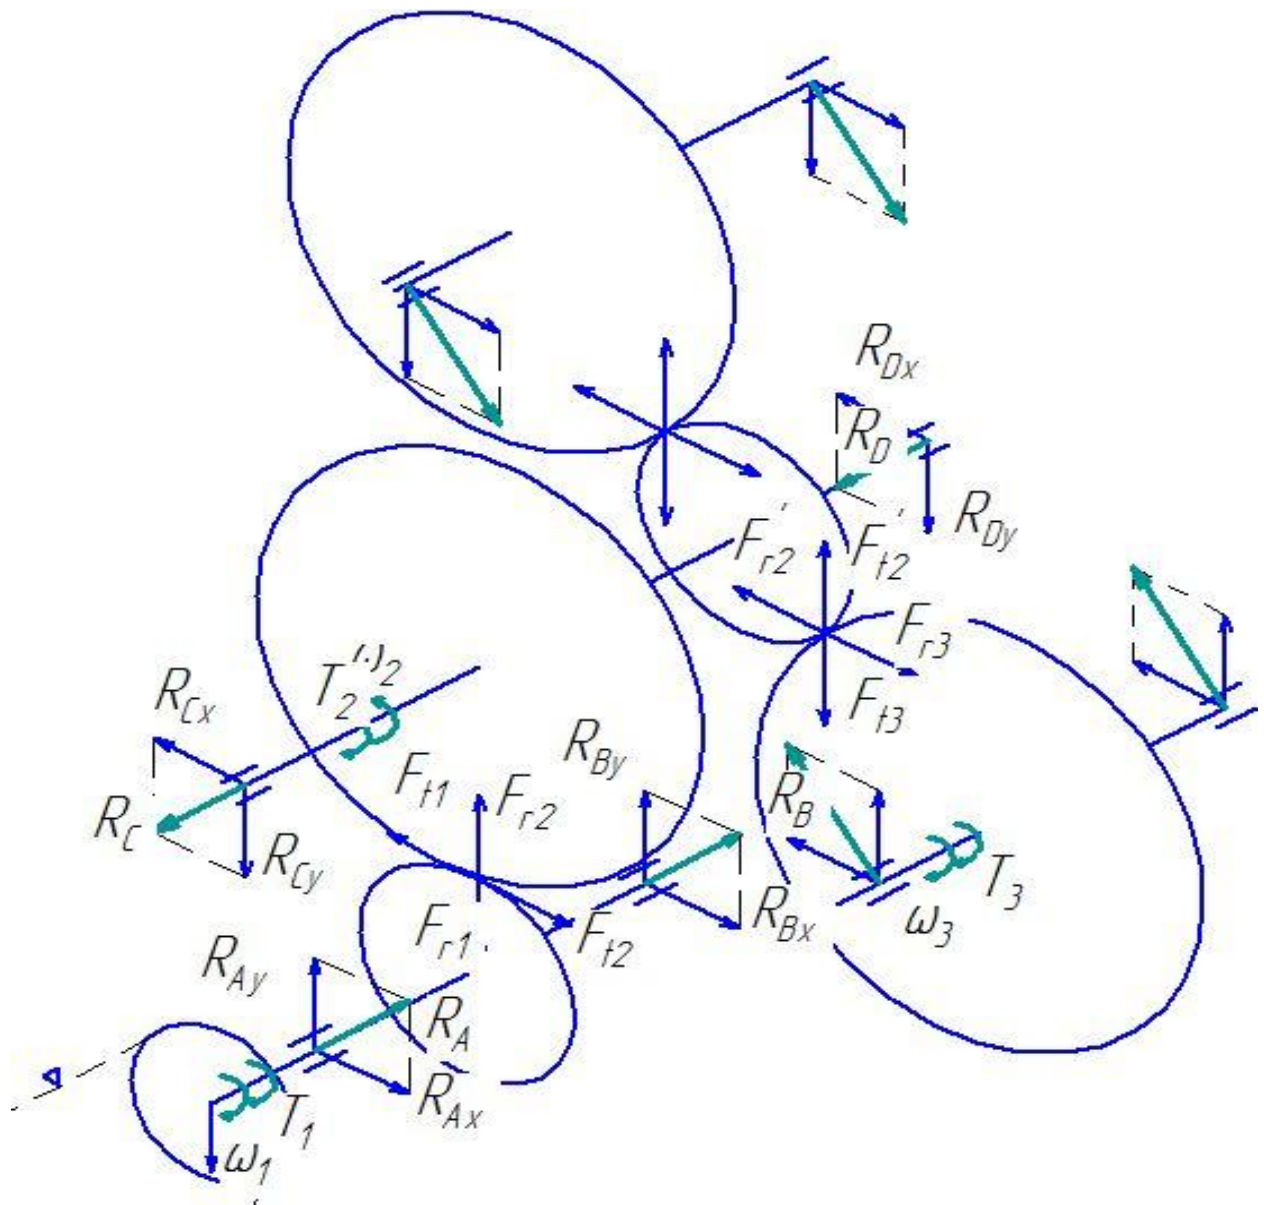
Схема навантаження валів циліндричного двухступеневого редуктора
